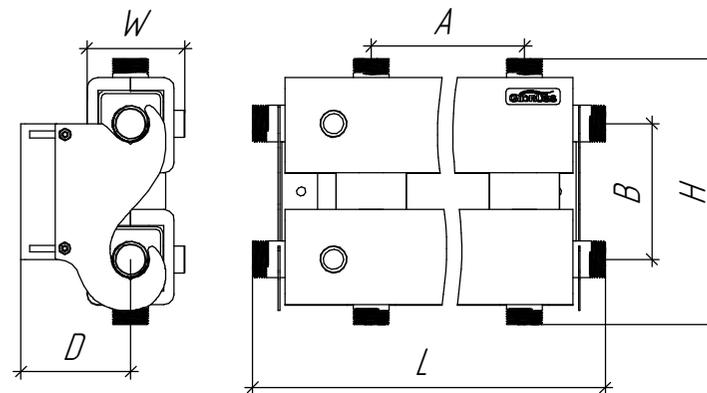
Габаритно-присоединительные размеры кольцевых коллекторов RM-60
